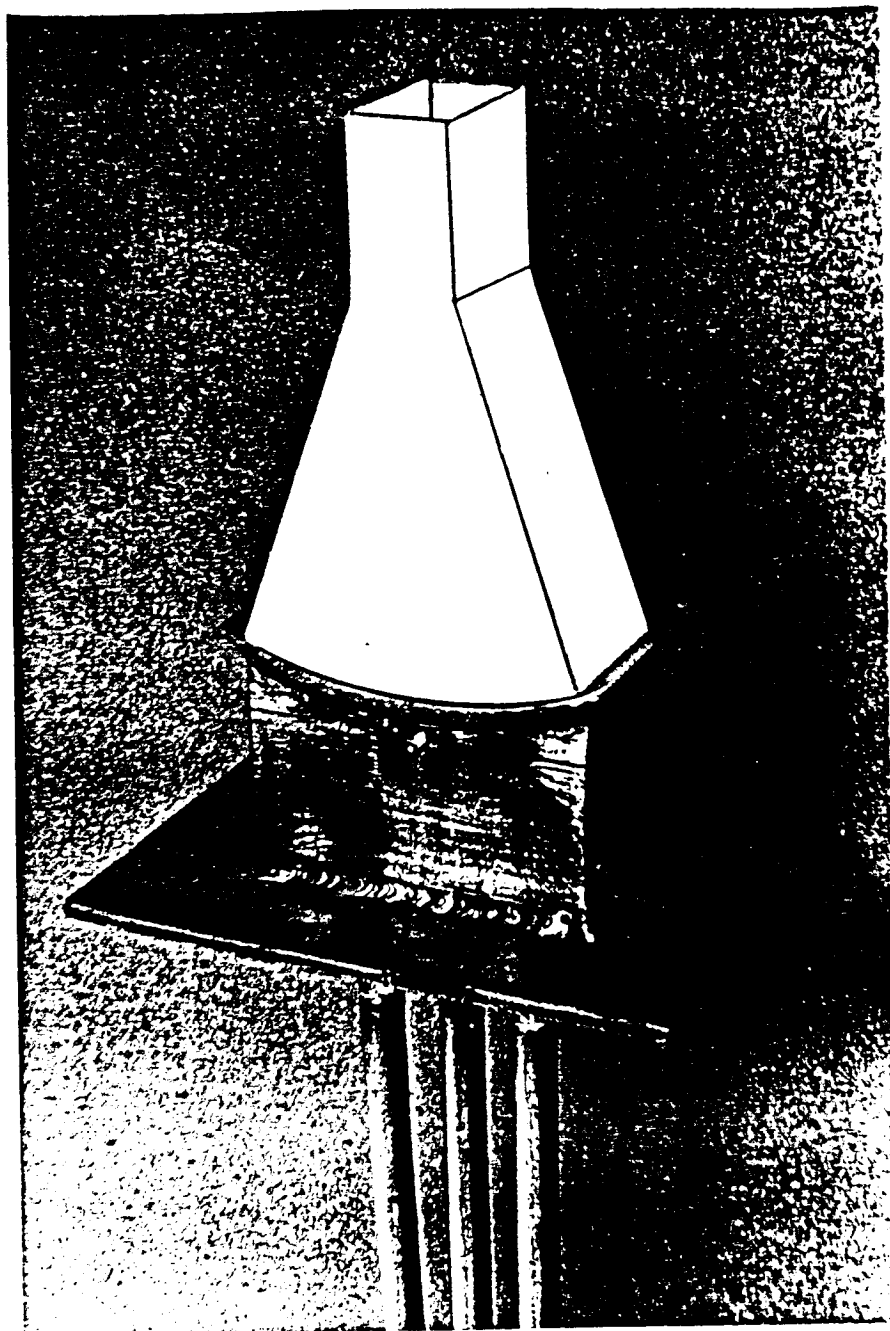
Montagem final do conjunto formado pelo molde, câmara de refrigeração e sistema de refrigeração.
